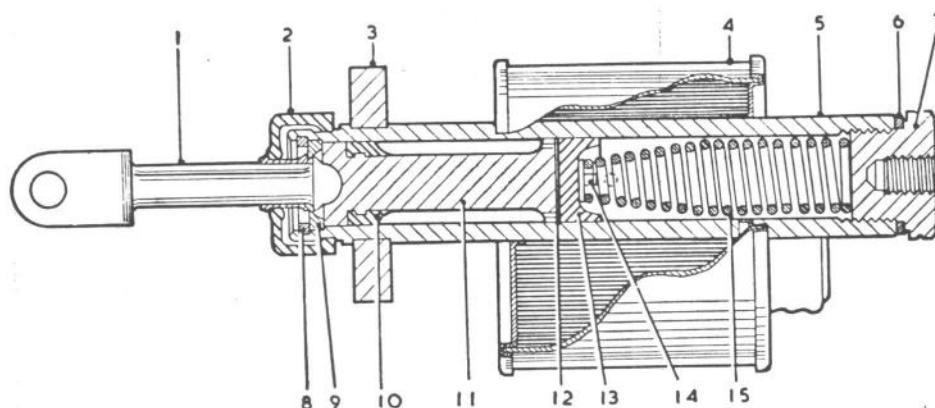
Sección en el cilindro principal de mando del embrague.
